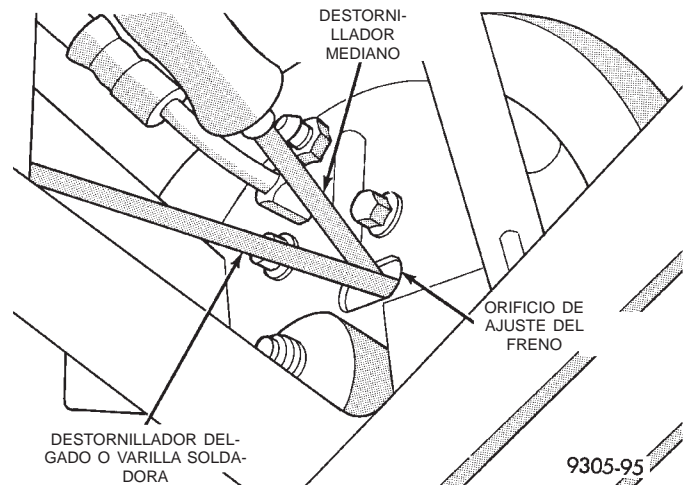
Ajuste del tambor de freno con la herramienta C-3784
